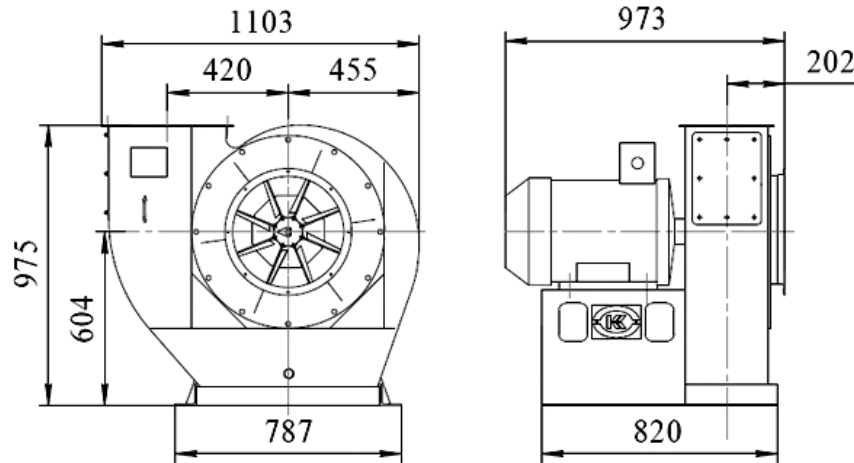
Вентиляторы ВРП-115-49-5,6. Габаритные размеры
